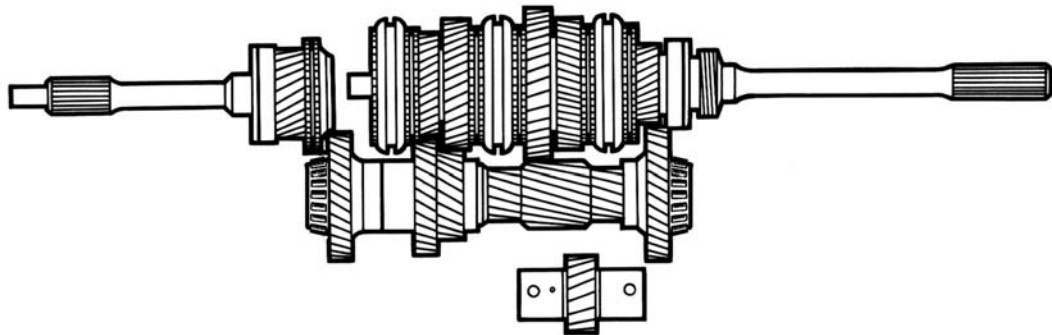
Валы и шестерни коробки передач после их сборки
